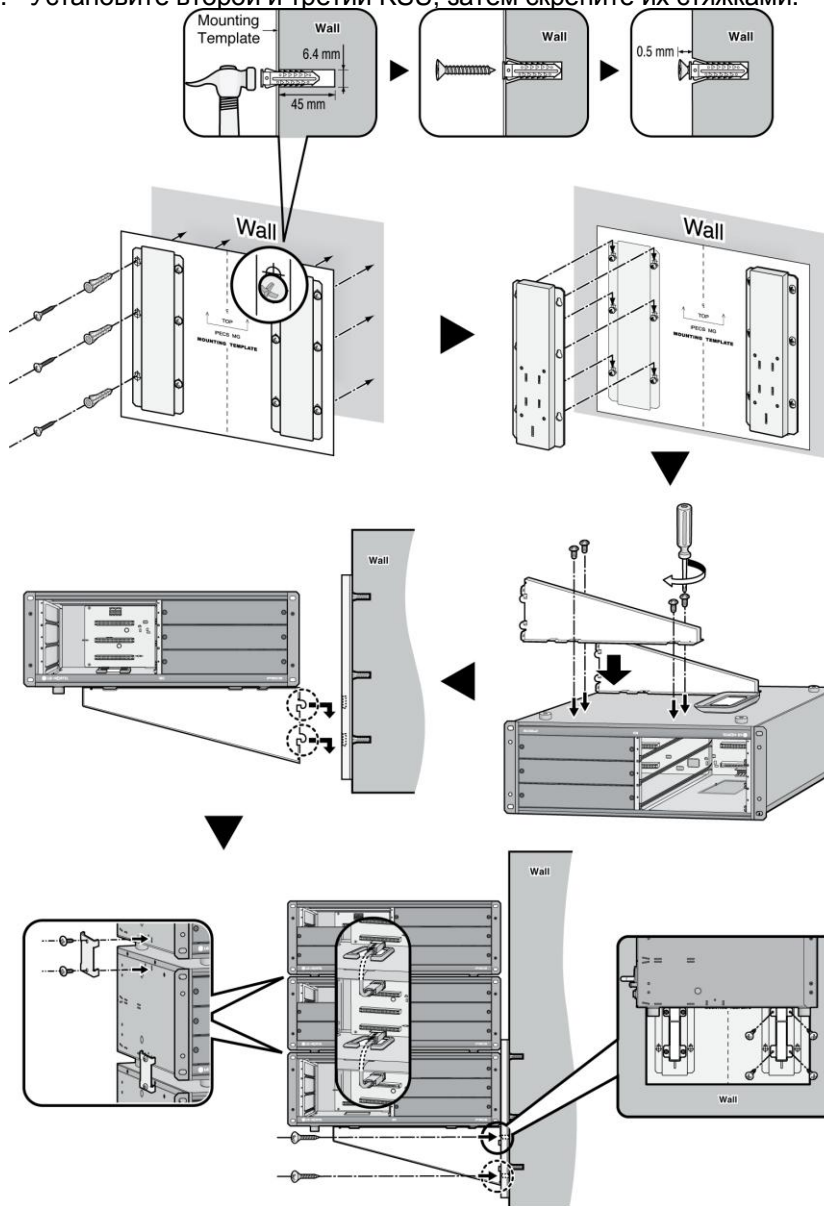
Монтаж дополнительных KSU на стену
